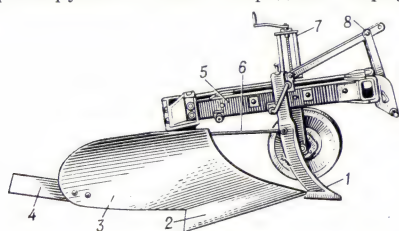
Кустарниково-болотный плуг: 1 — черенковый нож; 2 — лемех; 3 — отвал; 4 — перо; 5 — рама; 6 — прут; 7 — винтовой механизм регулирования опорного колеса; 8 — навеска плуга.
